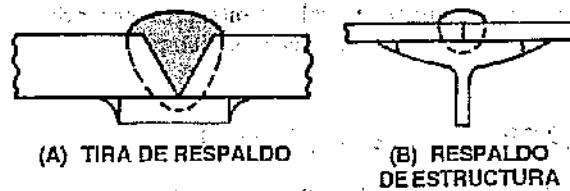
Respaldo de metal fusible para una soldadura
